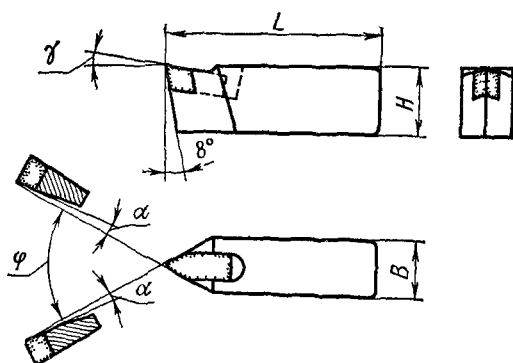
Резьбовой резец для нарезания резьбы вихревым способом.
